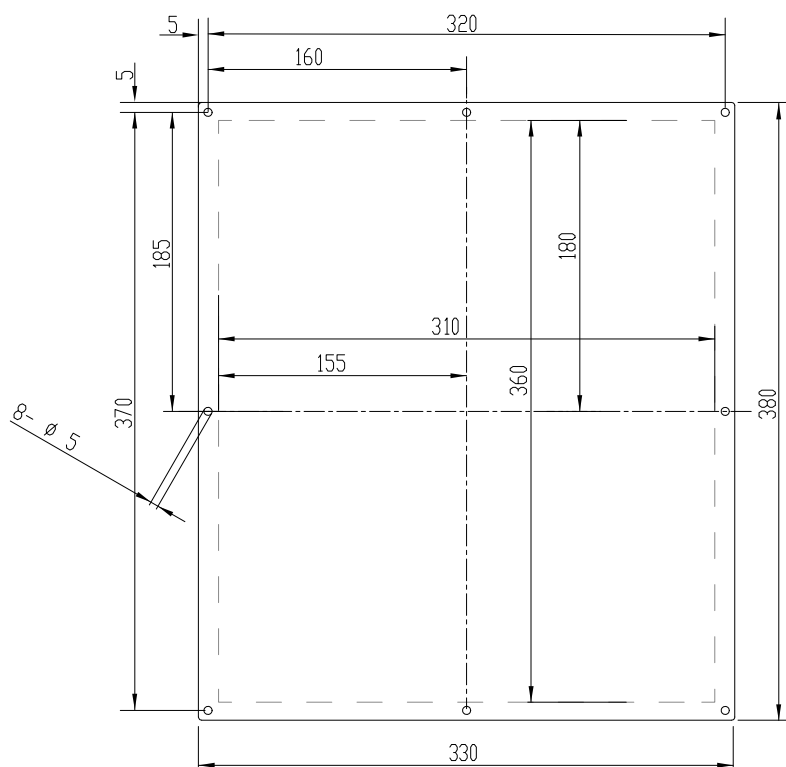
Рекомендуемый монтажный чертеж размеров отверстия для шкафа из листового металла – верхняя панель цельного контроллера N5
